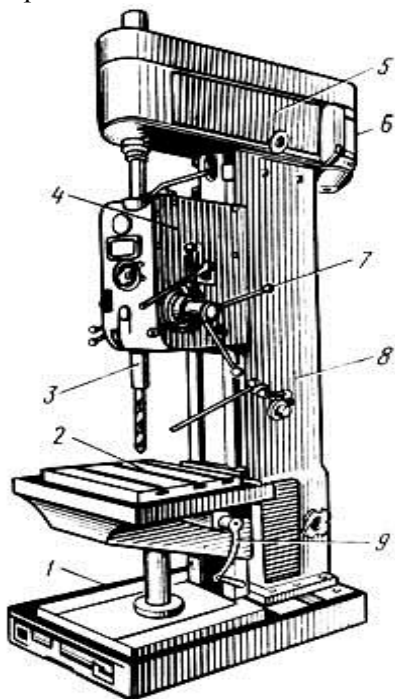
Вертикально-сверлильный станок 2А135: 1 - плита, 2 - стол, 3 - шпиндель, 4 - коробка подачи, 5 - шпиндельная головка 6 - электродвигатель, 7 - штурвал, 8 - станина, 9 – рукоятка
